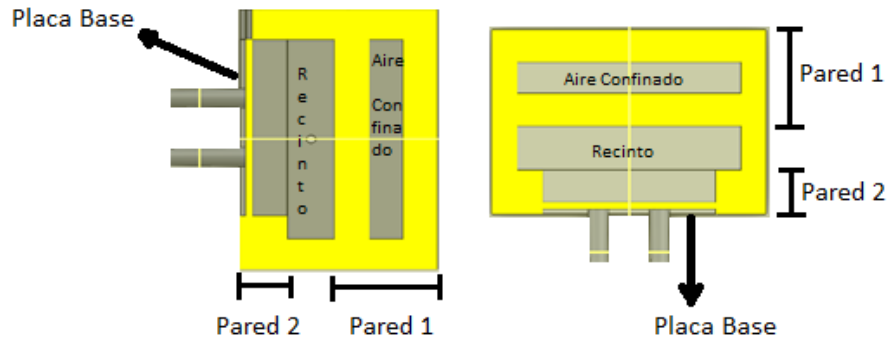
Espesores de pared 1 y 2 en cm. Corte transversal y en planta (Fuente propia)
